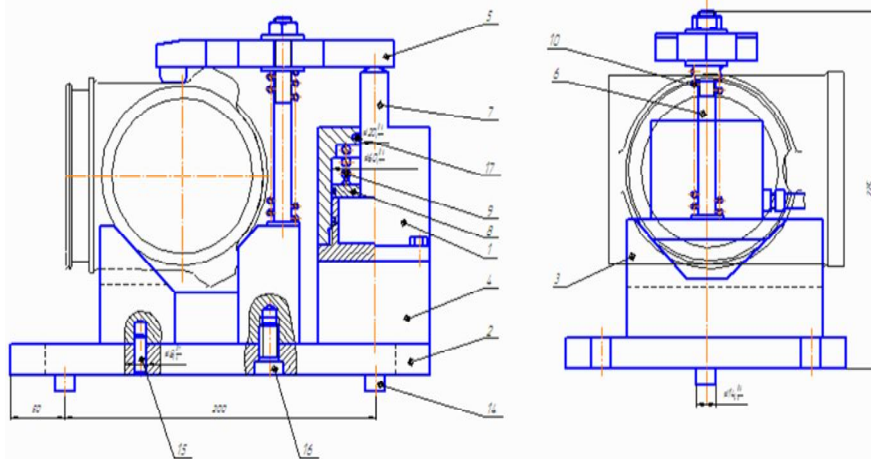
Наладка станка IP500МФ4 на изготовление цилиндра перфоратора ПТ48А (операции 12-15)
